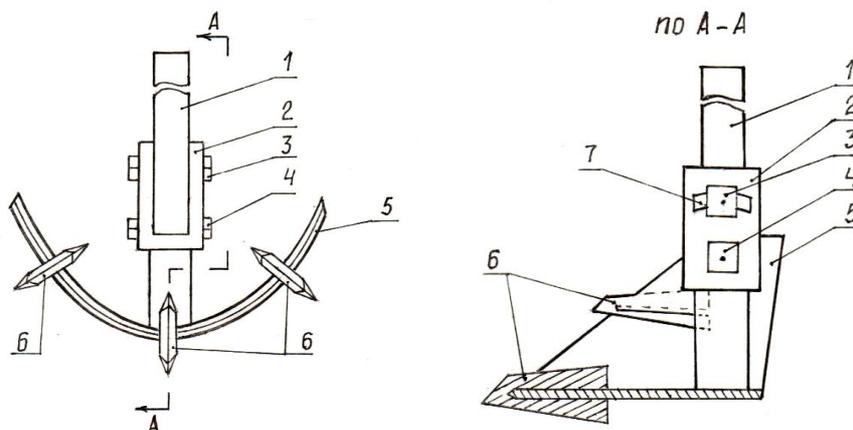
Рабочий орган культиватора для обработки почвы в бороздах: а) вид спереди; б) вид сбоку.
